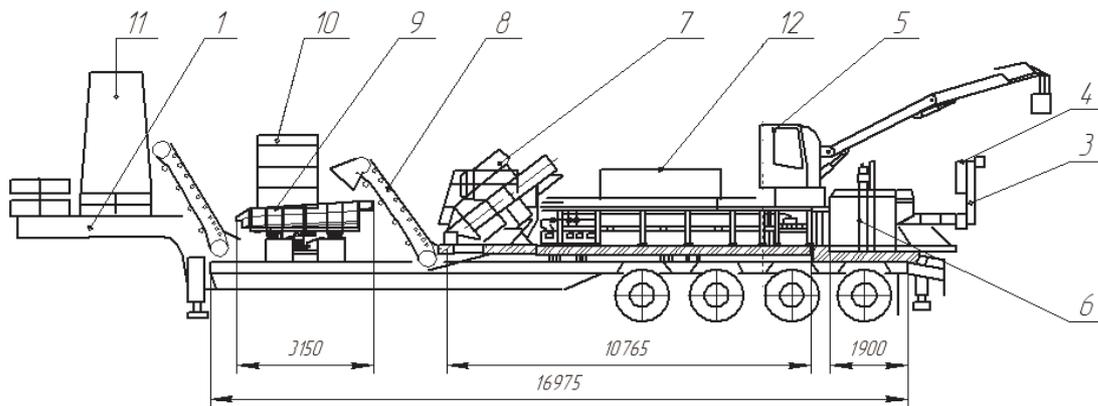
Модель экономичного мобильного комплекса для производства щепы и газа для топлива (общий вид): 1 – трейлер (полуприцеп-тяжеловоз (СAB 931826-000080-03); 2 – гидроманипулятор (ОМТЛ-97 – 04К); 3 – приемный лоток; 4 – пильная шина; 5 – кабина; 6 – окорочный станок; 7 – рубительная машина (дисковая резцовая МРР-500А); 8 – конвейер скребковый; 9 – сортировочная установка (СЩ-100-1); 10 – конвейер скребковый; 11 – газогенератор; 12 – силовая установка.
